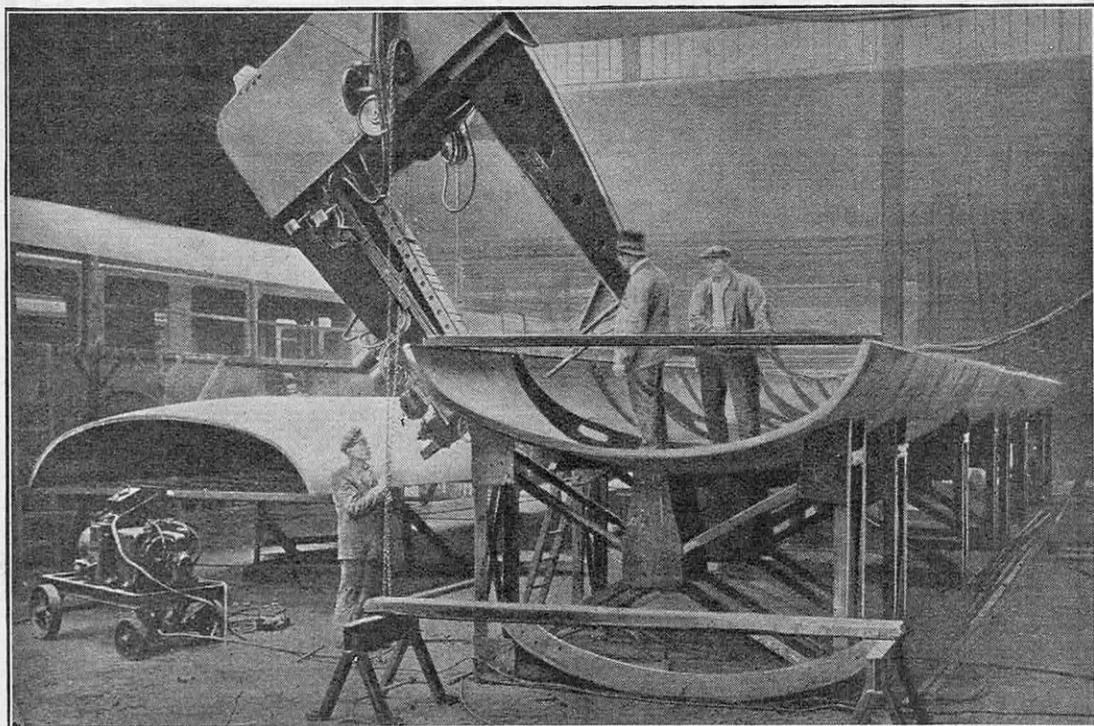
COMMENT ON APPLIQUE LA SOUDURE ÉLECTRIQUE PAR RÉSTANCE (PAR POINTS) DANS LA FABRICATION DES TOITS DE VOITURES DE CHEMIN DE FER
